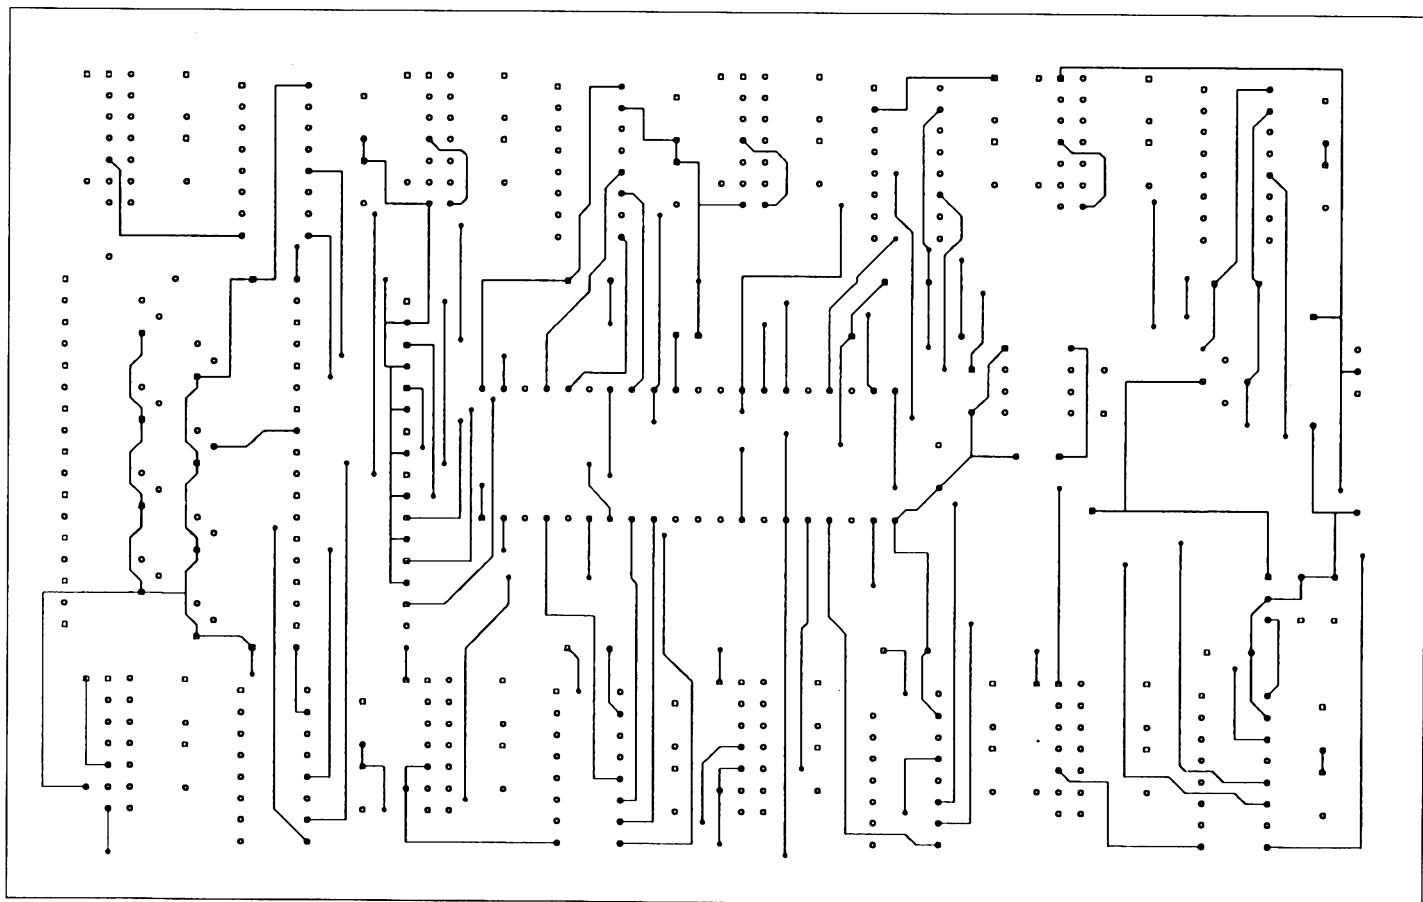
PCB layout knooppuntregelaar, soldeerzijde.
